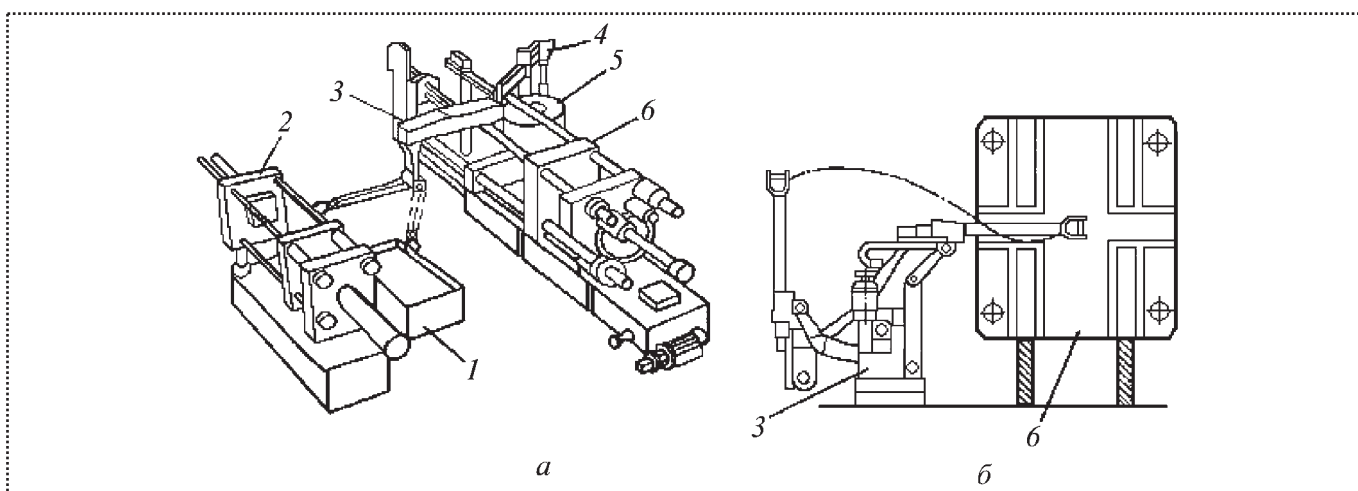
Варианты РТК для производства заготовок методом литья под давлением с подвесным (а) и напольным (б) ПР: 1 – ванна для охлаждения отливок; 2 – горизонтальный обрубной пресс; 3 – разгрузочный ПР; 4 – дозатор; 5 – печь с расплавом; 6 – МЛД
